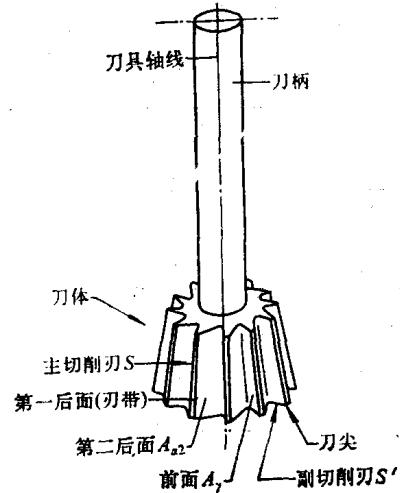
直柄单角铣刀切削部分上的切削刃和表面
